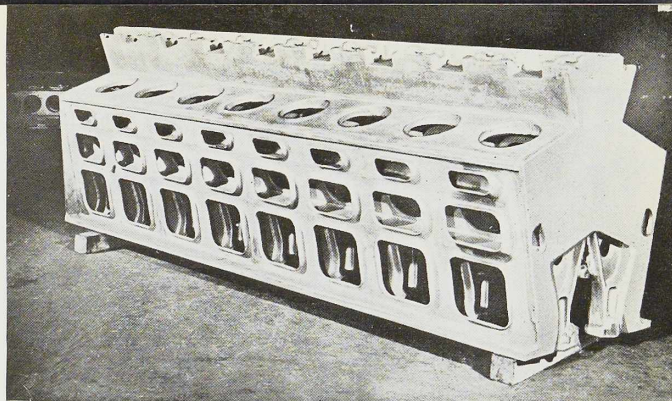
Bâti soudé d'un moteur Diesel à 16 cylindres en « V ».
